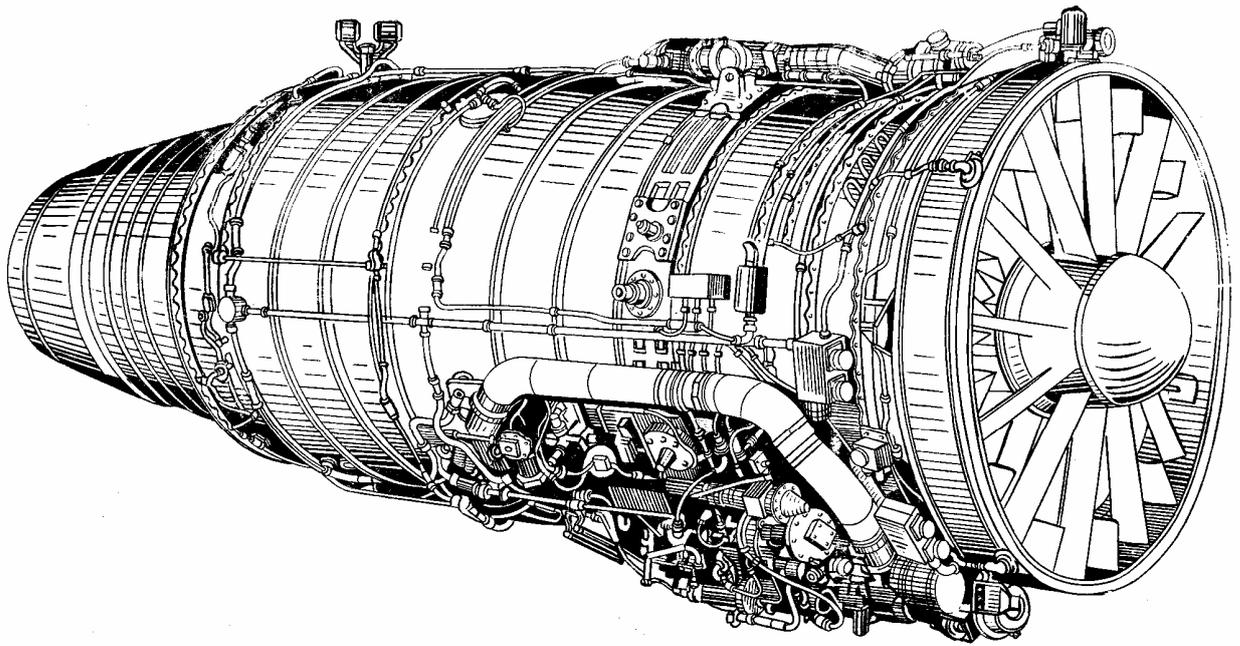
Двигатель НК-8-2У с соплом (вид справа)
